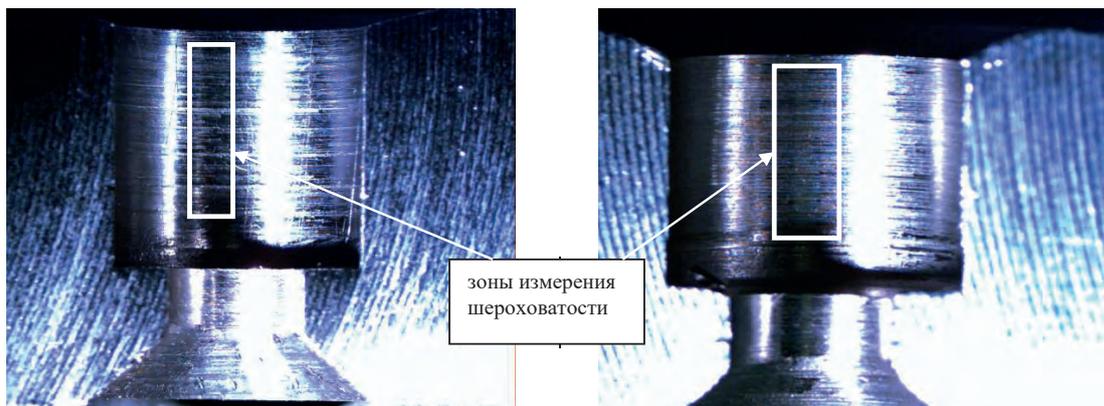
Вид поверхности посадочного отверстия оправы, образец № 1
